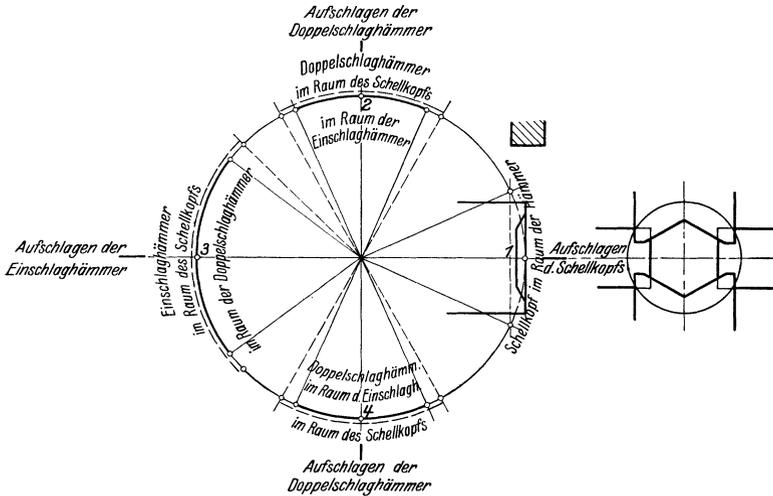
Arbeitswegschau­bild der Bolzenkopfschmiedemaschine.
